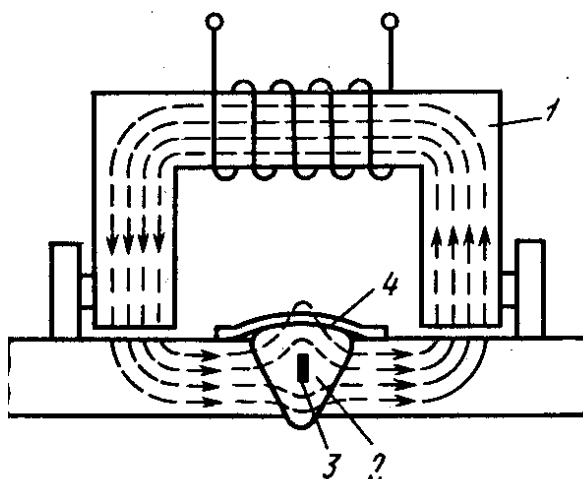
Схема магнитографического контроля: 1. Намагничивающее устройство; 2. Сварной шов; 3. Дефект в сварном шве; 4. Магнитная пленка.
